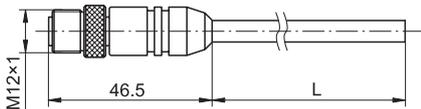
Cable de conexión BKS-S105-CP-...
